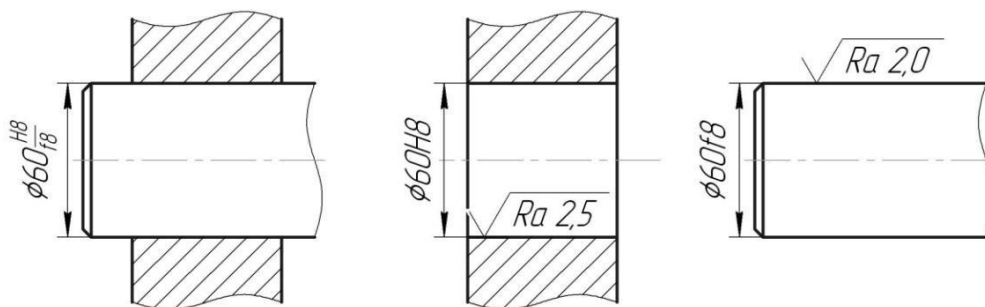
Обозначение посадки и полей допусков деталей на чертежах
